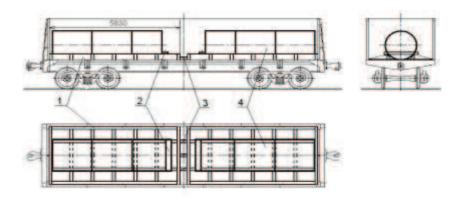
1- рама; 2- упорная балка; 3- распорный брусок; 4- рулон
